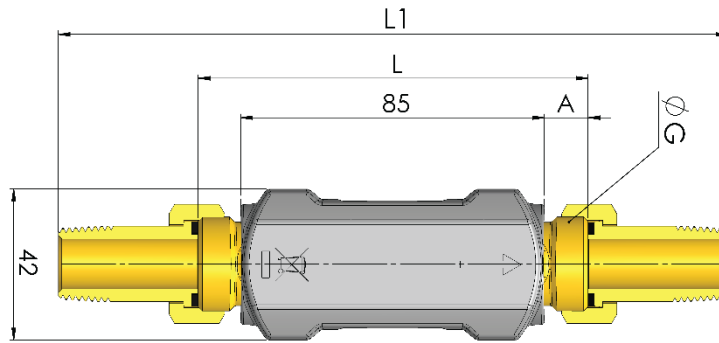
Maßskizzen der ULTRAFLOW® 44-Gewindezähler Typ 65-4-XXHX-XXX mit Verschraubungen.
